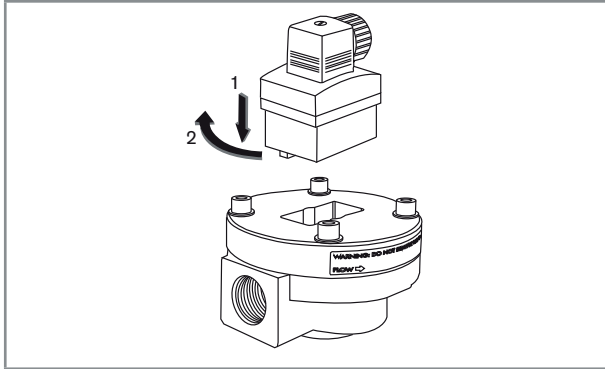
Montage des SE30 Ex auf ein Sensor-Fitting Typ S070 oder Typ S077
